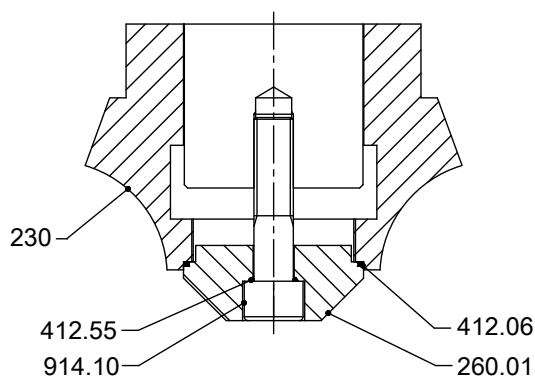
Крепление рабочего колеса M100 × 2 (для проточной части К 500-632, К 500-640)
